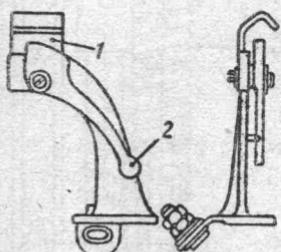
Держатель положительного угля: 1 — переставной угольник; 2 — рукоятка зажима угля
